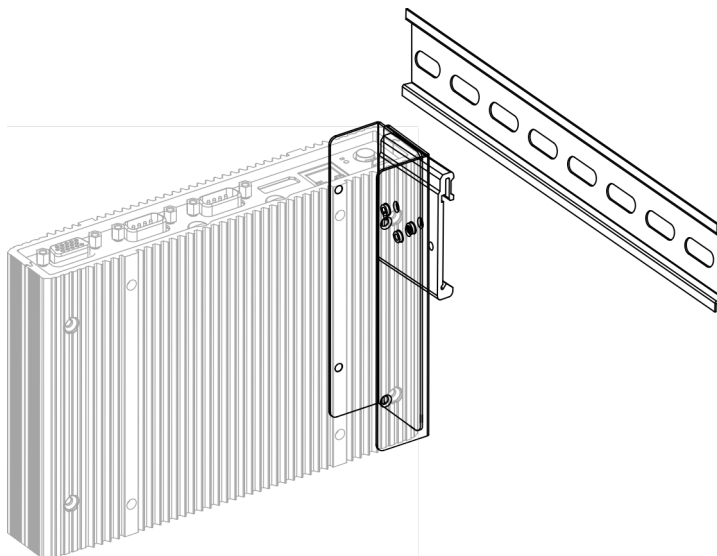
Montaggio di KC-M20 sulla guida DIN
